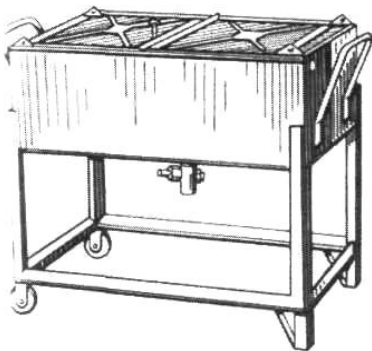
Ванна передвижная для мойки мелких деталей ОМ -1316
